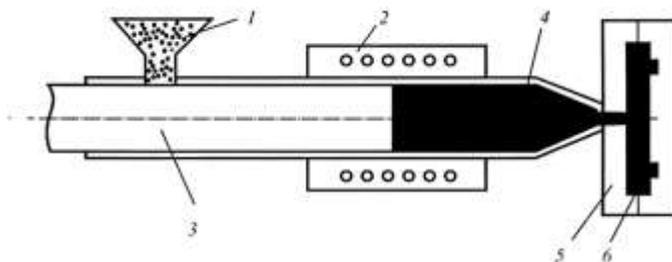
Схема литья под давлением: 1 – гранулят; 2 – электронагреватели; 3 – поршень (плунжер); 4 – расплав; 5 – пресс-форма; 6 – отливка
